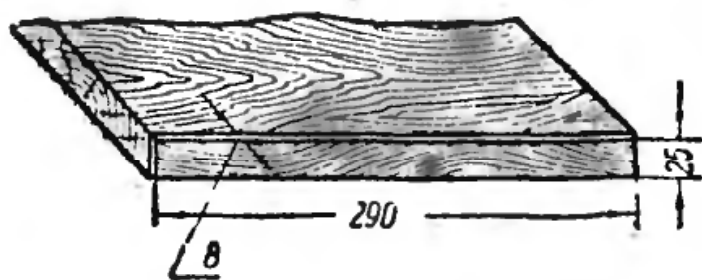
Разметка и обработка заготовки для боковых брусков рамок № 27 и 28.
